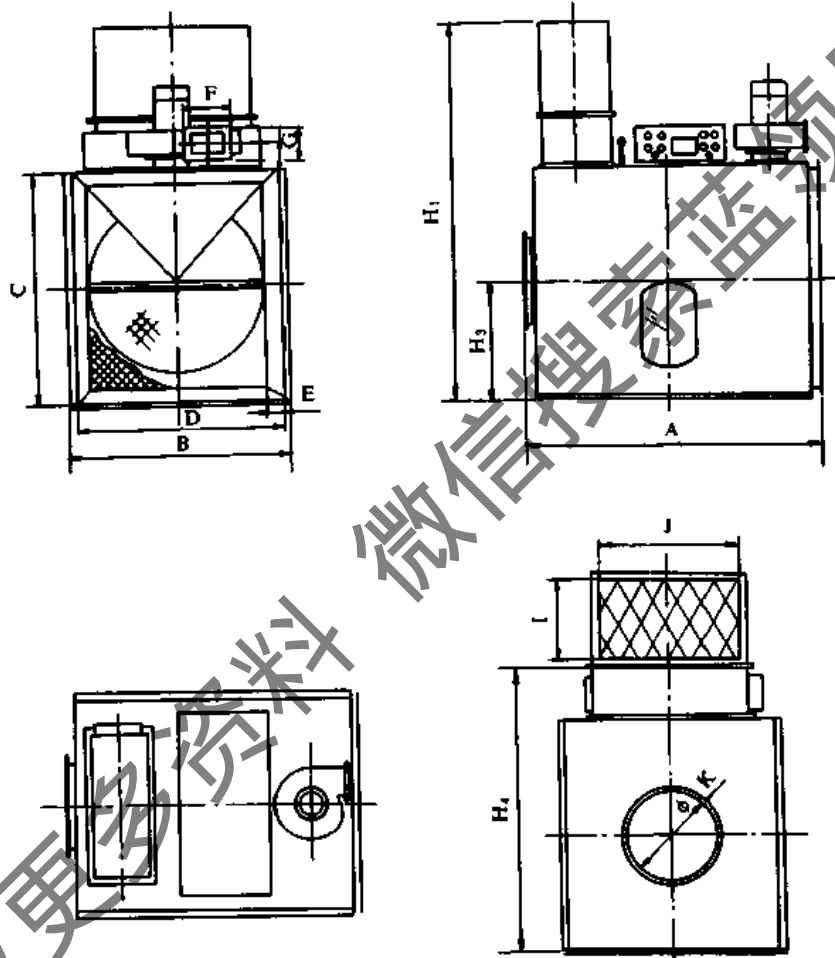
ZS-10-60D 型除湿机外形尺寸
